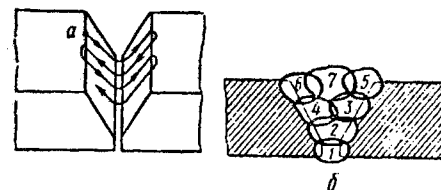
Сварка стыковых швов. а — однослойного; б — многослойного; 1—7 — последовательность наложения швов
